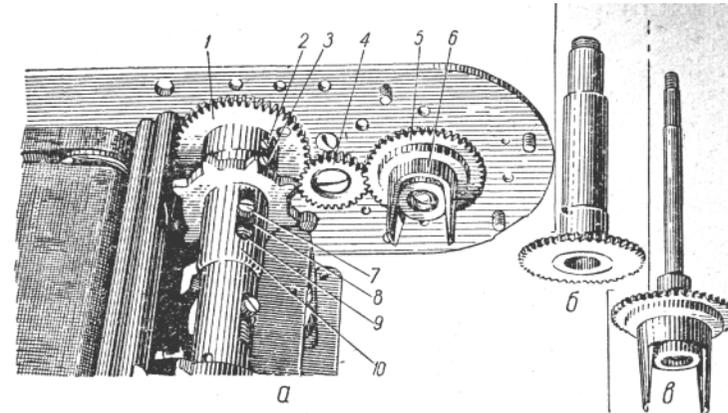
Нижняя сторона заводного механизма: а — в собранном виде; б — зубчатое колесо со втулкой; в — зубчатое колесо и фрикцион вилки намотки.
